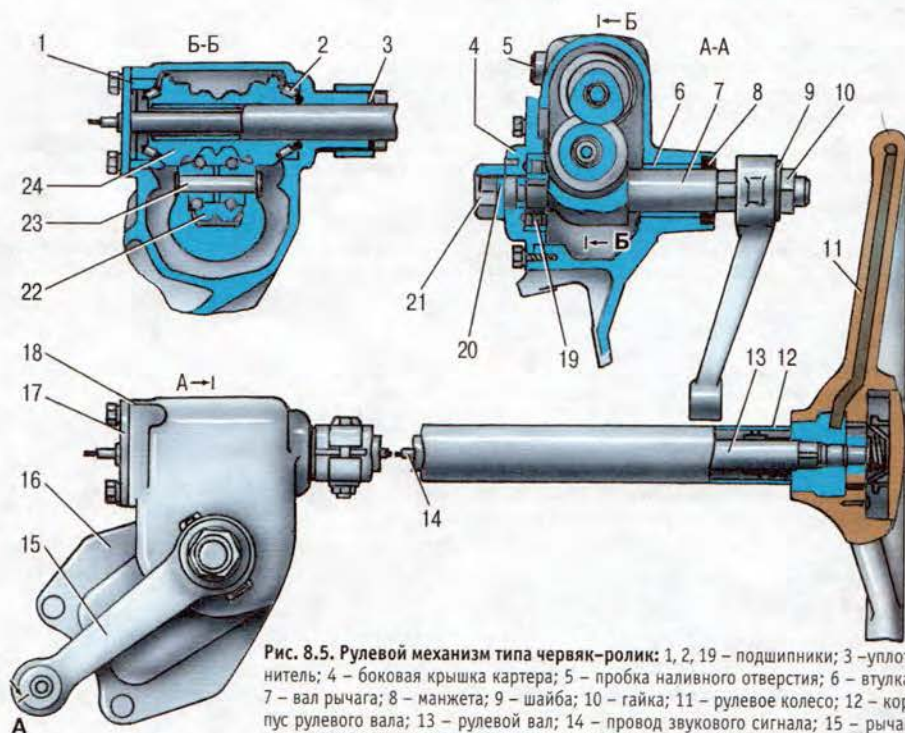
Рулевой механизм типа червяк-ролик: 1, 2, 19 – подшипники; 3 – уплотнитель; 4 – боковая крышка картера; 5 – пробка наливного отверстия; 6 – втулка; 7 – вал рычага; 8 – манжета; 9 – шайба; 10 – гайка; 11 – рулевое колесо; 12 – корпус рулевого вала; 13 – рулевой вал; 14 – провод звукового сигнала; 15 – рычаг; 16 – картер; 17 – нижняя крышка; 18 – регулировочные прокладки подшипников червяка; 20 – регулировочный винт зазора в зацеплении; 21 – колпачковая гайка; 22 – ролики; 23 – ось ролика; 24 – червяк
